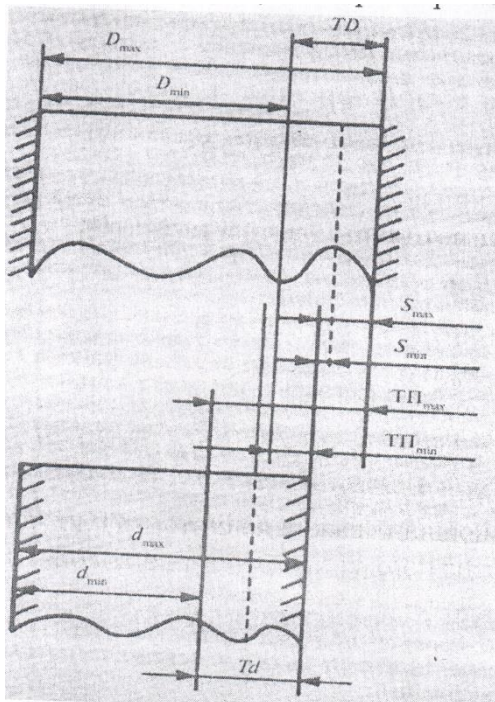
Схема формирования допуска зазора соединения цилиндр – поршень при групповой взаимозаменяемости.
